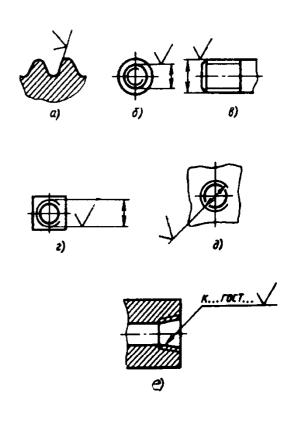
Обозначение шероховатости поверхности профиля резьбы
